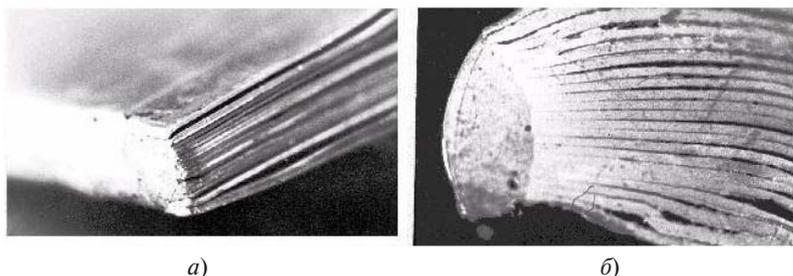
Наплавка трехфазной дугой торца пакета шинопровода из тонколистового алюминиевого сплава:
